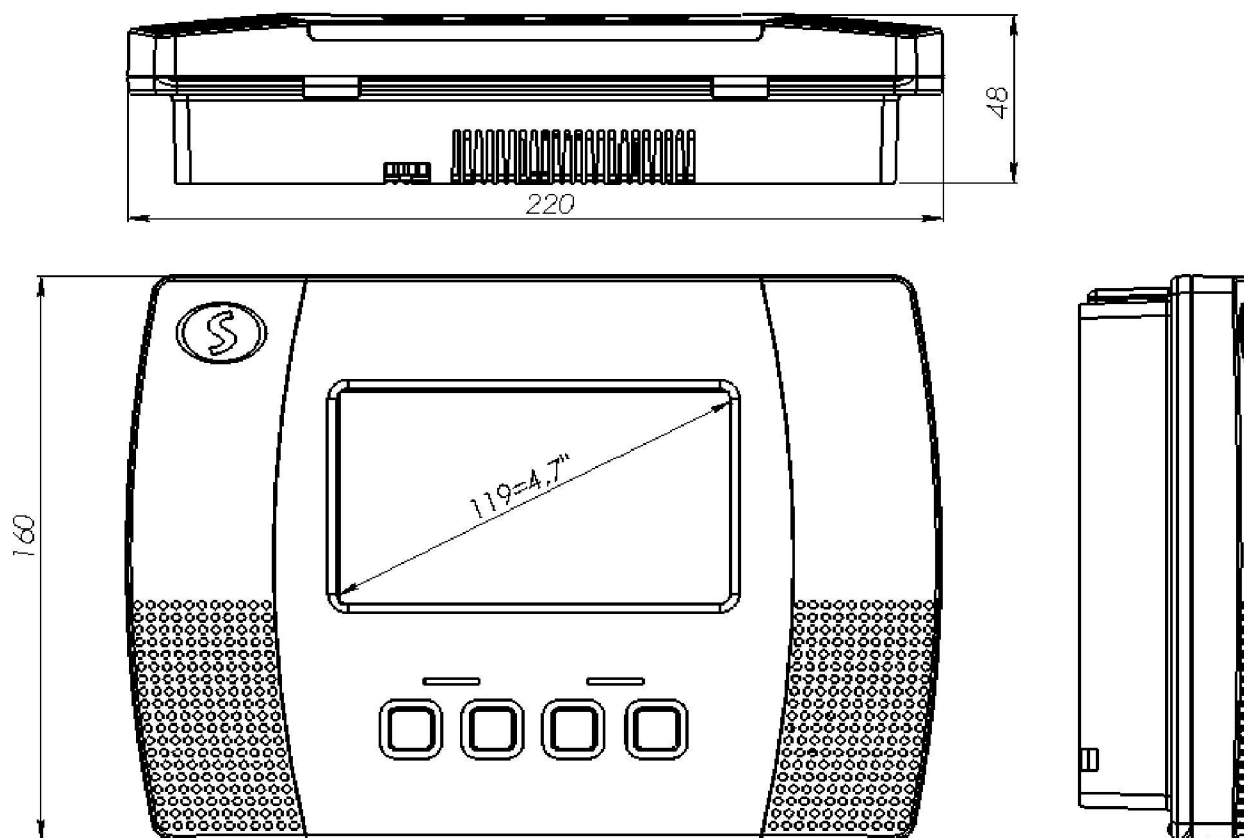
Внешний вид и габаритные размеры ППКОП "Лунь-19"
